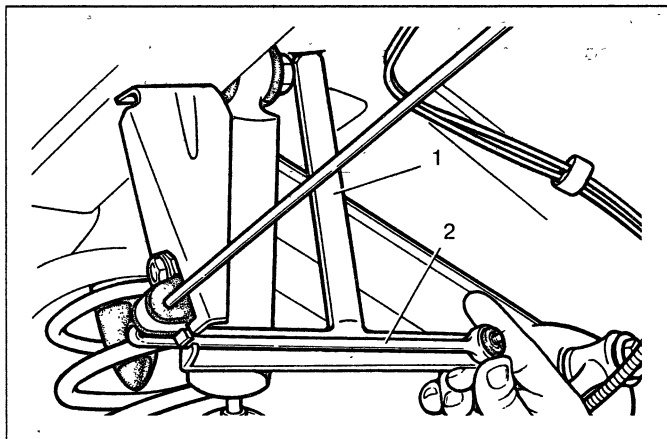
Установка приспособления 67.7820.9519 для регулировки положения регулятора давления задних тормозов: 1 – приспособление 67.7820.9519; 2 – рычаг привода регулятора давления
